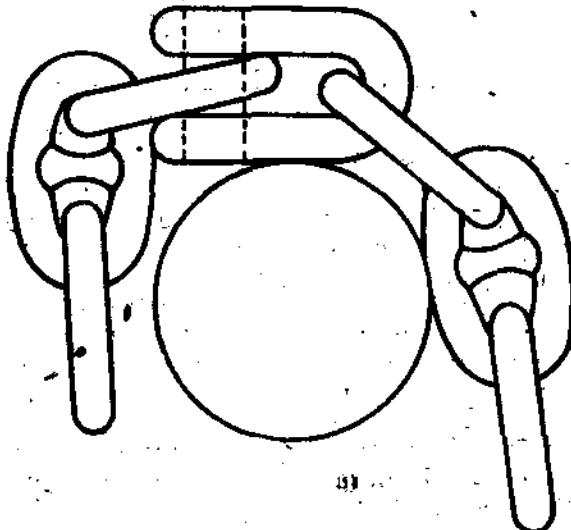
Схема расположения скобы на барабане, весьма опасное для прочности соединения,
